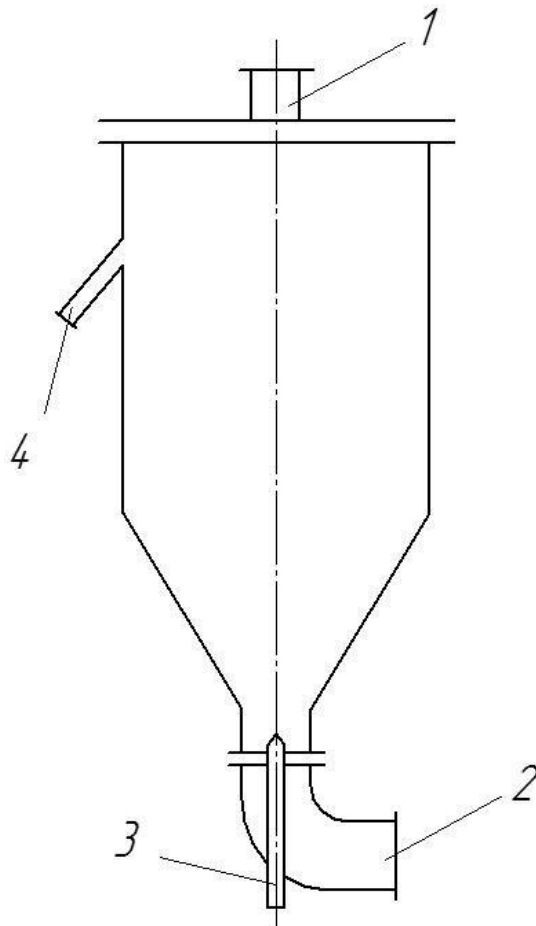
Схема конічного апарата з фонтануючим шаром [53]:
